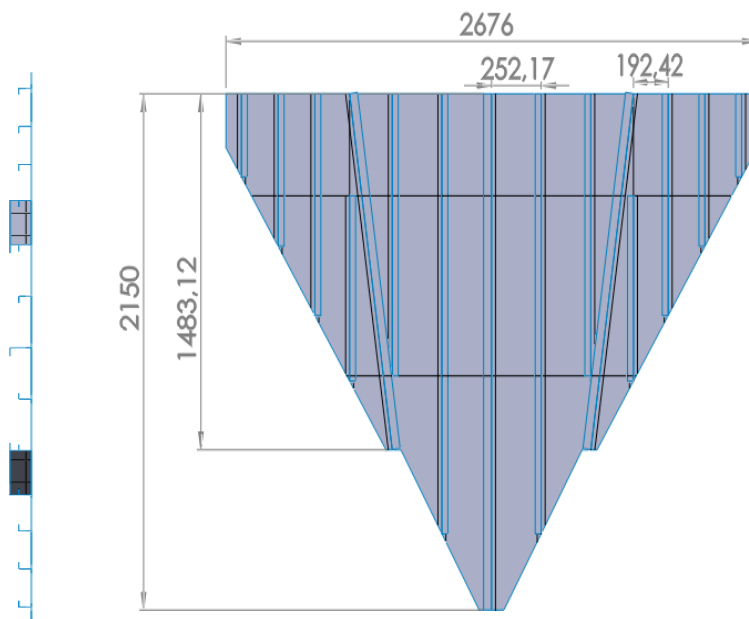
Desenho técnico incompleto da antepara n°20
